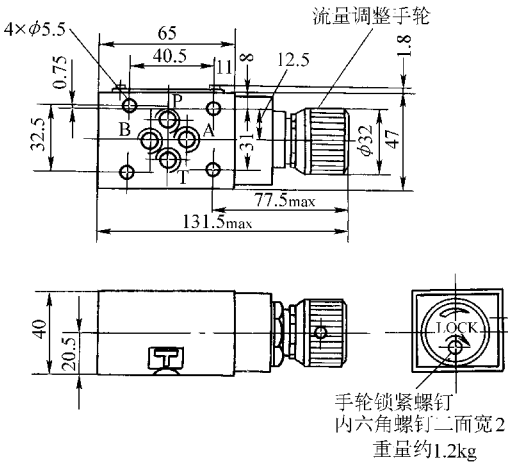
MSP-01 型叠加式节流阀的外形尺寸
